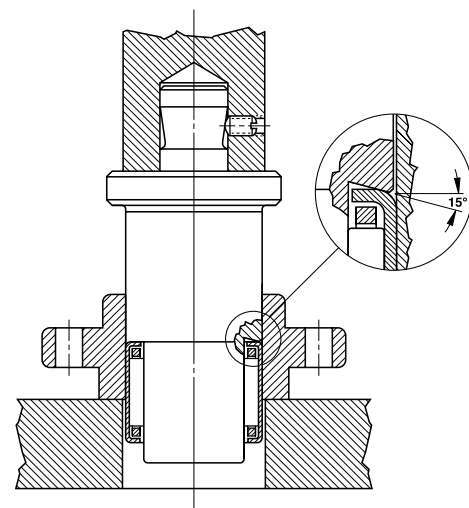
Ausbau aus einem Gehäuse ohne Schulter
